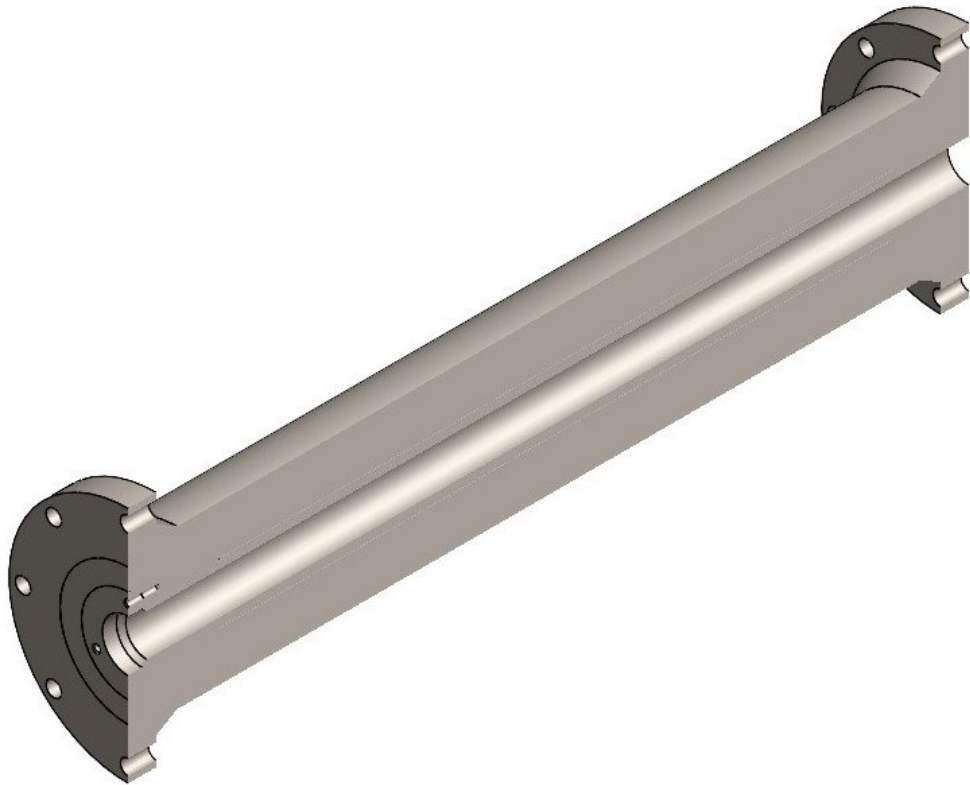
Модель базової конструкції корпусу у розрізі
